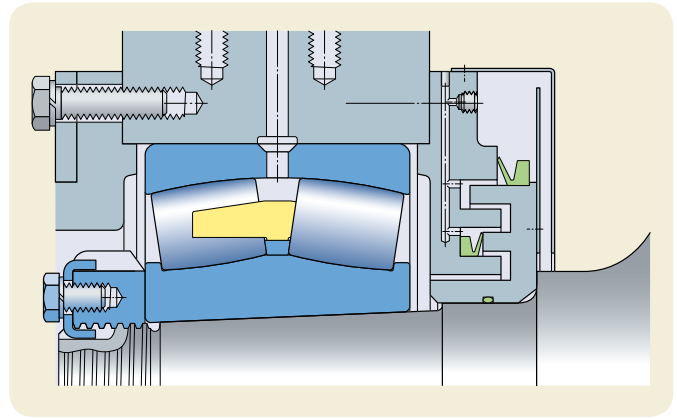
Ajout d'un couvercle, d'un disque rotatif et d'un joint V-ring supplémentaire sur un cylindre aspirant
